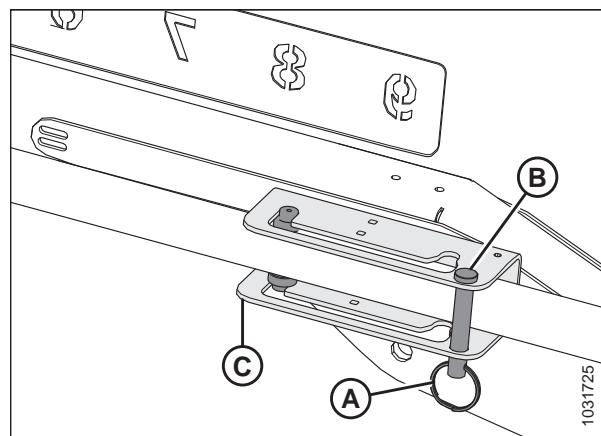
Цилиндр левого рычага — переднее положение
